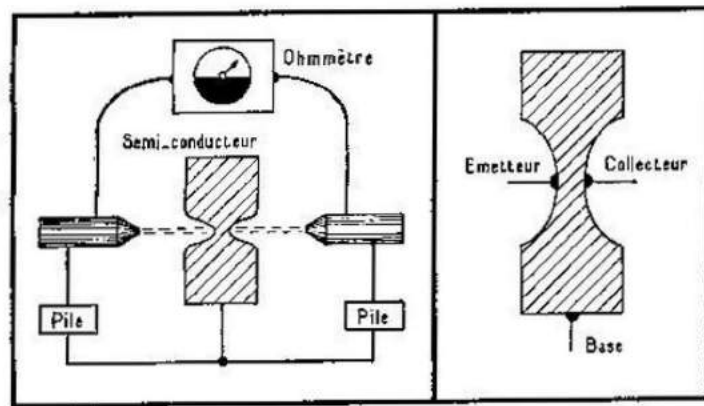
Procédé de fabrication du transistor à barrière de surface et vue en coupe d'un tel transistor.
